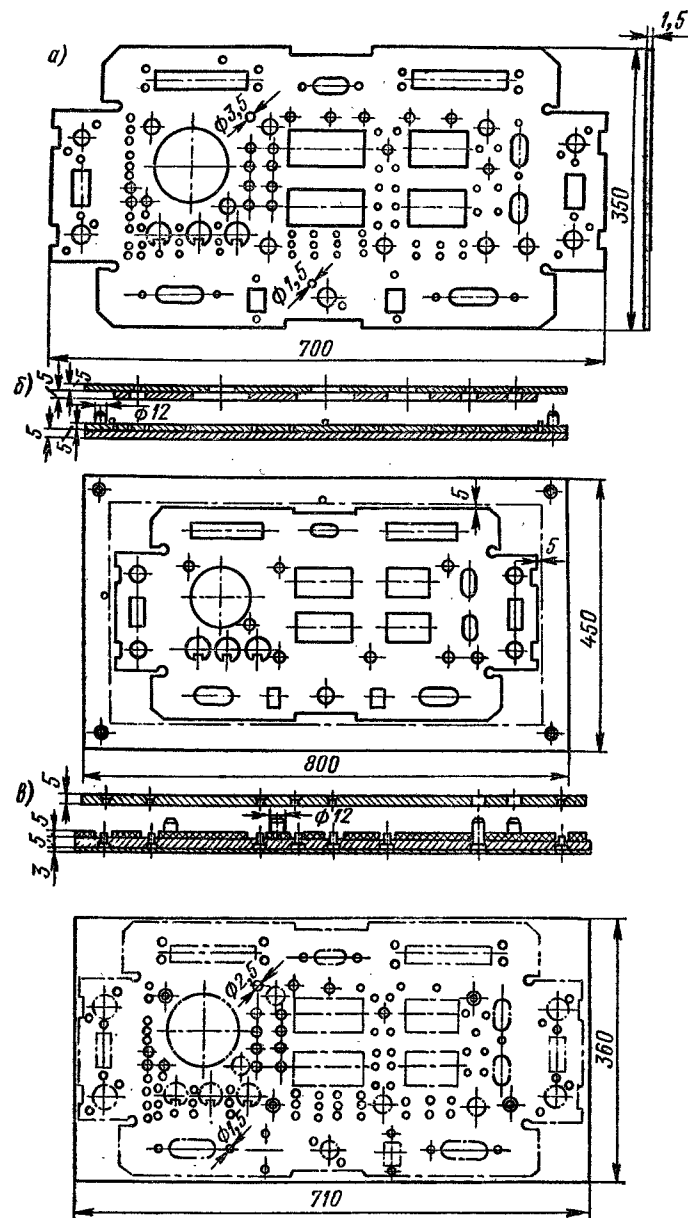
Листовые штампы для крупногабаритных деталей; а — штампуемая деталь; б — штампы для вырубki и пробивки; в — штамп для пробивки мелких отверстий
